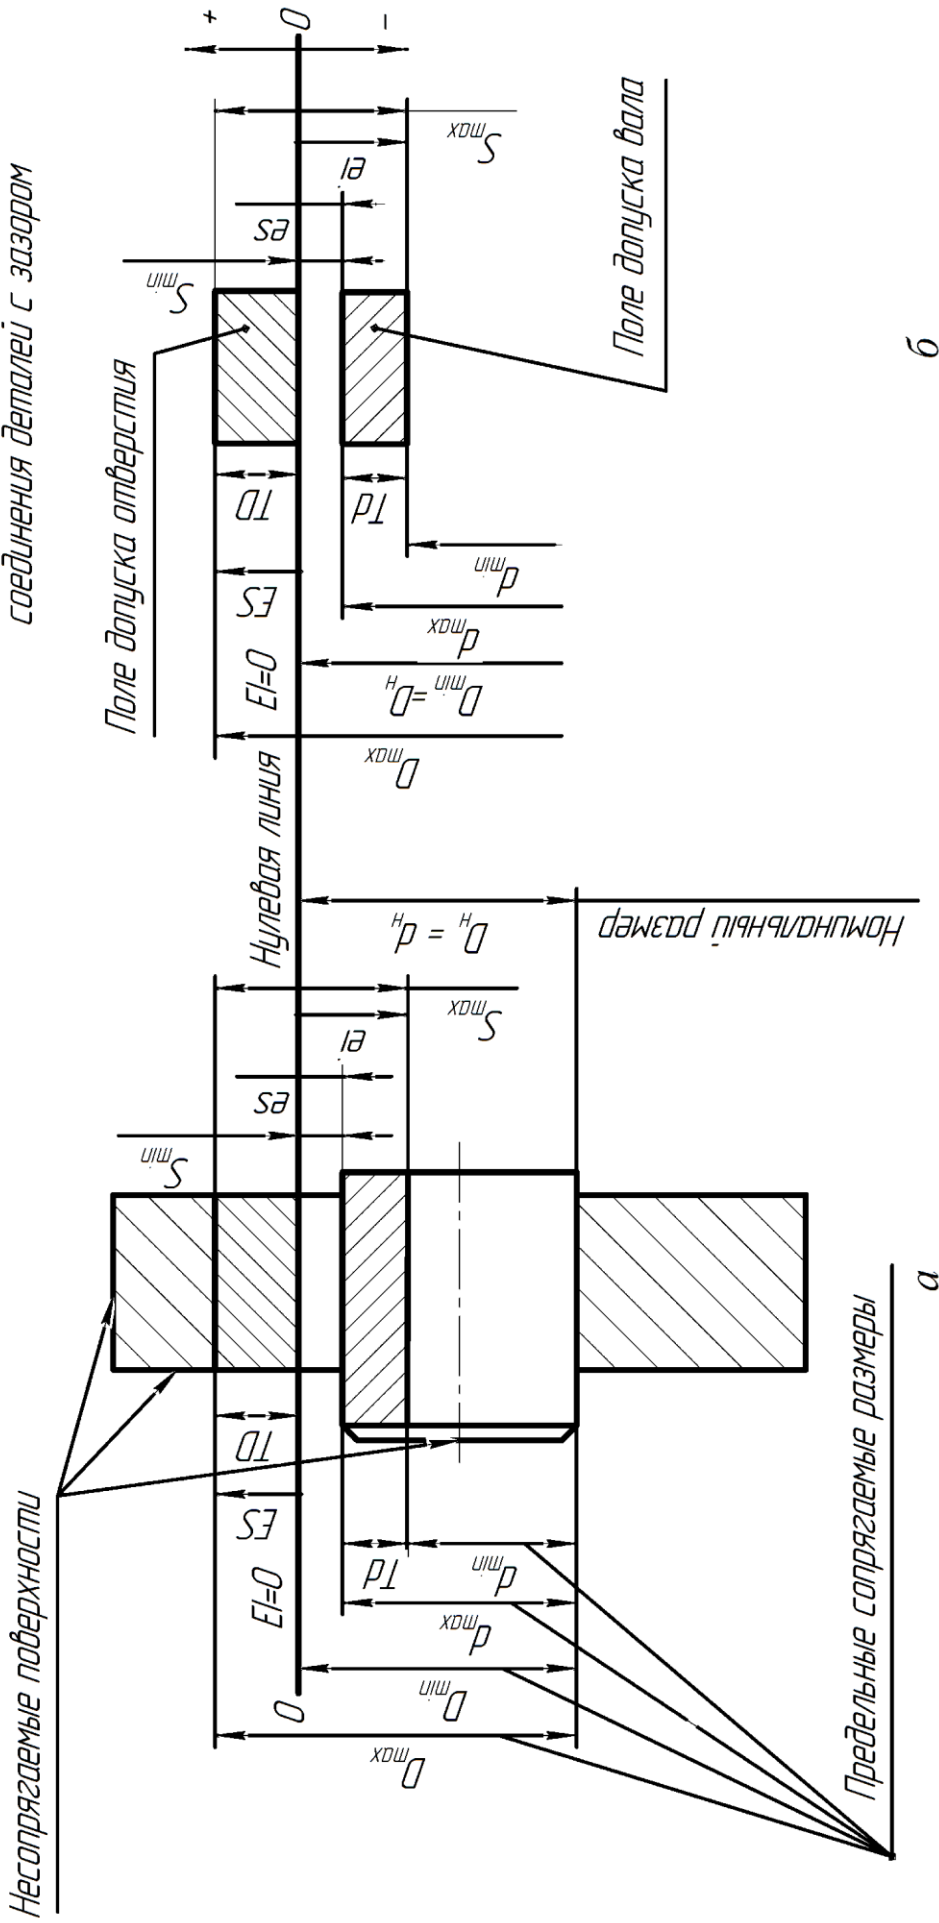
Графическое представление: а - соединение деталей с зазором; б - схема расположения полей допусков соединения деталей с зазором; TD - допуск размера отверстия; TD - допуск размера вала; ES - верхнее отклонение отверстия; EI - нижнее отклонение отверстия; eS - верхнее отклонение вала; eI - нижнее отклонение вала; D_{max} - наибольший предельный размер отверстия; D_{min} - наименьший предельный размер отверстия; d_{max} - наибольший предельный размер вала; d_{min} - наименьший предельный размер вала; S_{max} - наибольший зазор соединения; S_{min} - наименьший зазор соединения; D_H - номинальный размер отверстия; d_H - номинальный размер вала
